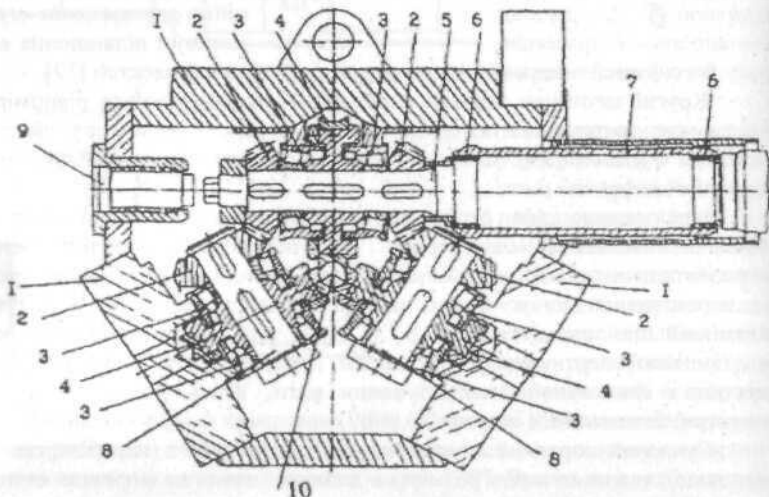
Кинематична схема приводу валків 1 - корпус кліті; 2 - конічна шестерня; 3 - радіальний підшипник; 4 - валок; 5 - провідний вал; 6 - шліцеве з'єднання; 7 - шліцевий вал; 8 - ведений вал; 9 - ключ для ручного проворота; 10 - калібр
